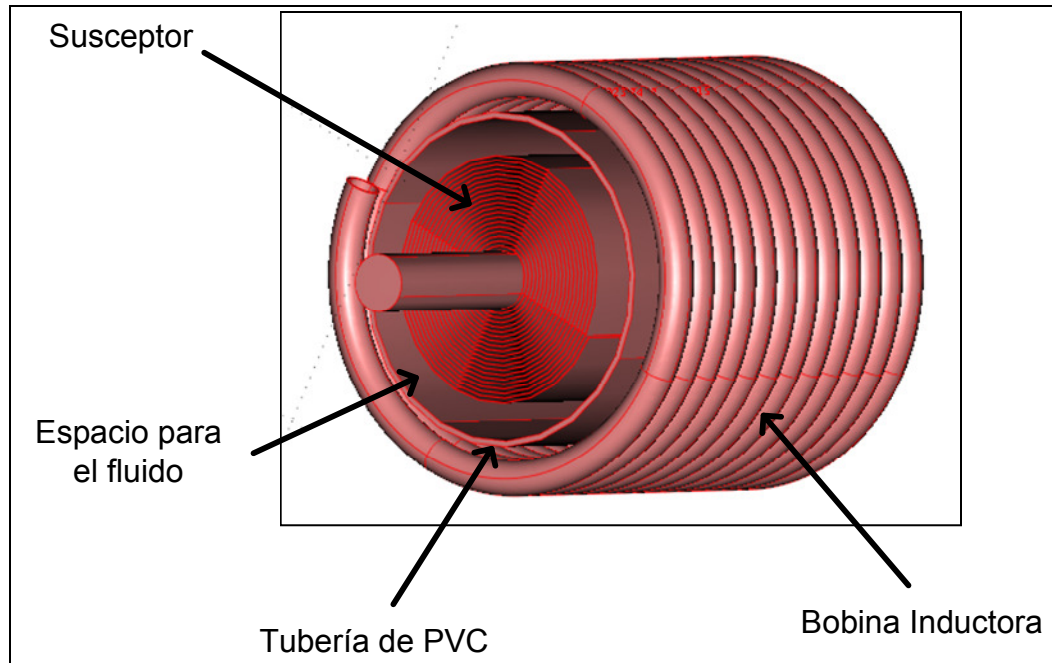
Principales Componentes del conjunto Bobina-Susceptor.
